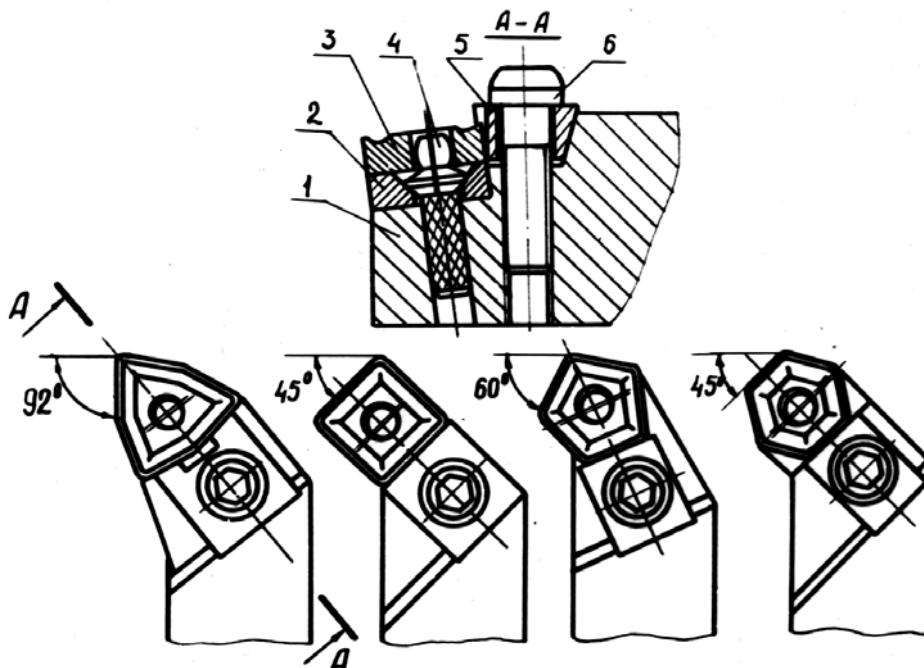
Резцы конструкции ВНИИИнструмента
